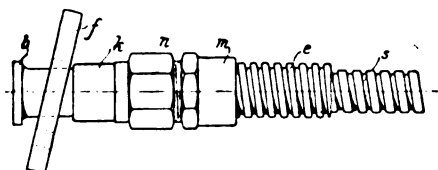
Aufgeschraubte Stopfbüchsenkupplung mit Innengewinde und eingeschraubtem Bordstutzen mit losem Flansch, nebst Endschutzhülse.
